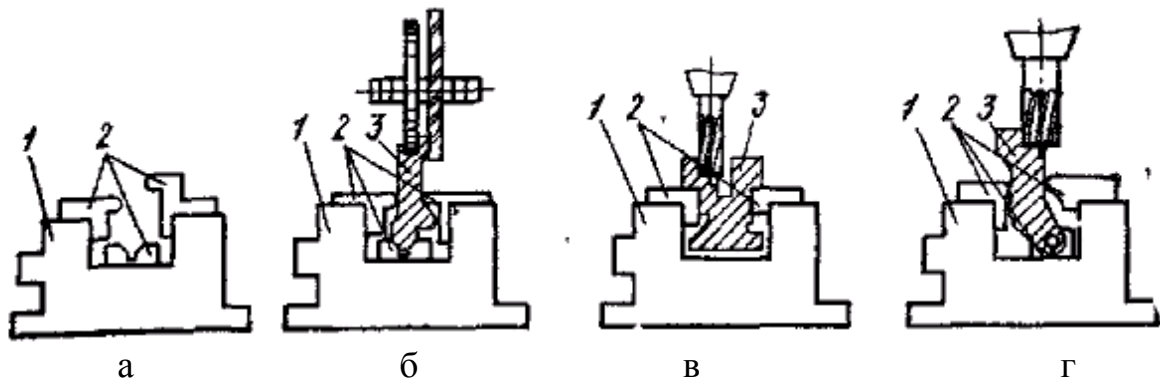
Схема универсально-наладочного приспособления (а) и его наладка для фрезерования: паза и плоскости у рычага (б); уступа в корпусе (в); уступа в рычаге (г).
